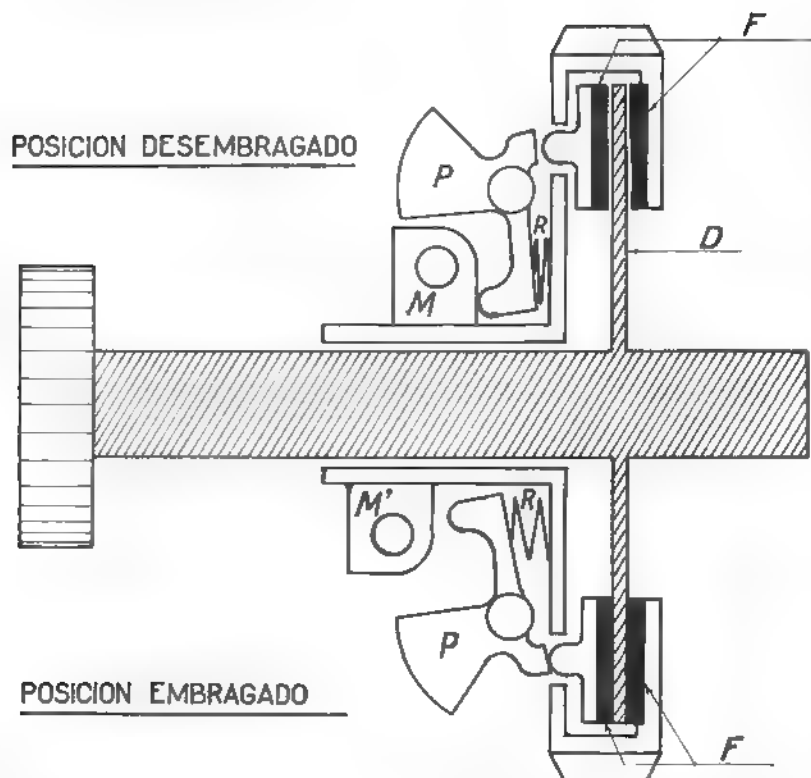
Esquema del embrague centrífugo Farman. El disco D , enlazado permanentemente con el motor, gira con él. Las coronas de fricción F , masas P y manguito MM' , constituyen un conjunto unido por engranajes al rotor del compresor. Cuando el piloto desplaza el manguito M a la posición M' , las masas P giran alrededor de su eje por la acción de los muelles R , estableciendo un contacto ligero con las coronas F , que lo establecen a su vez con el disco D , iniciándose el giro con resbalamiento del conjunto de que forma parte M . La fuerza centrífuga que se desarrolla en P aumenta progresivamente y con ella la presión de los discos de embrague, efectuándose totalmente el embrague en un tiempo de cinco a diez segundos.
